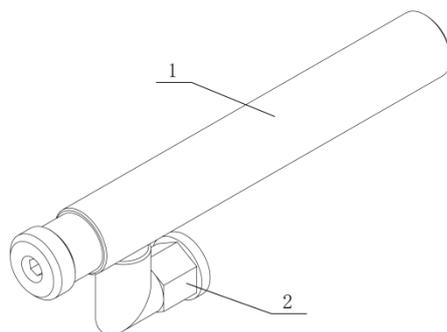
Верхний инструмент для глухих втулок и шпилек
